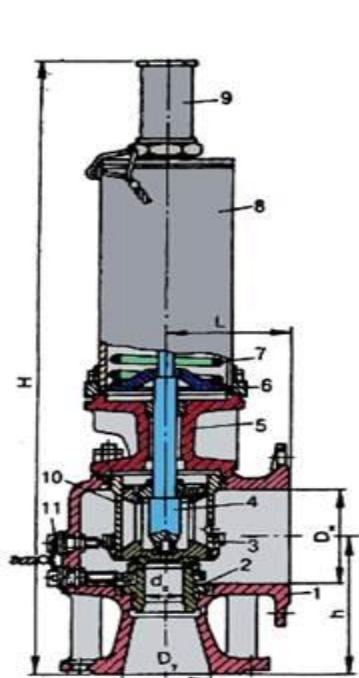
Клапан типа СПК4Р. 1 – корпус; 2 – сопло; 3 – золотник; 4 – шток; 5 – разделитель; 6 – опорная шайба; 7 – пружина; 8 – крышка; 9 – колпак; 10 – направляющая втулка; 11 – стопорный винт.
